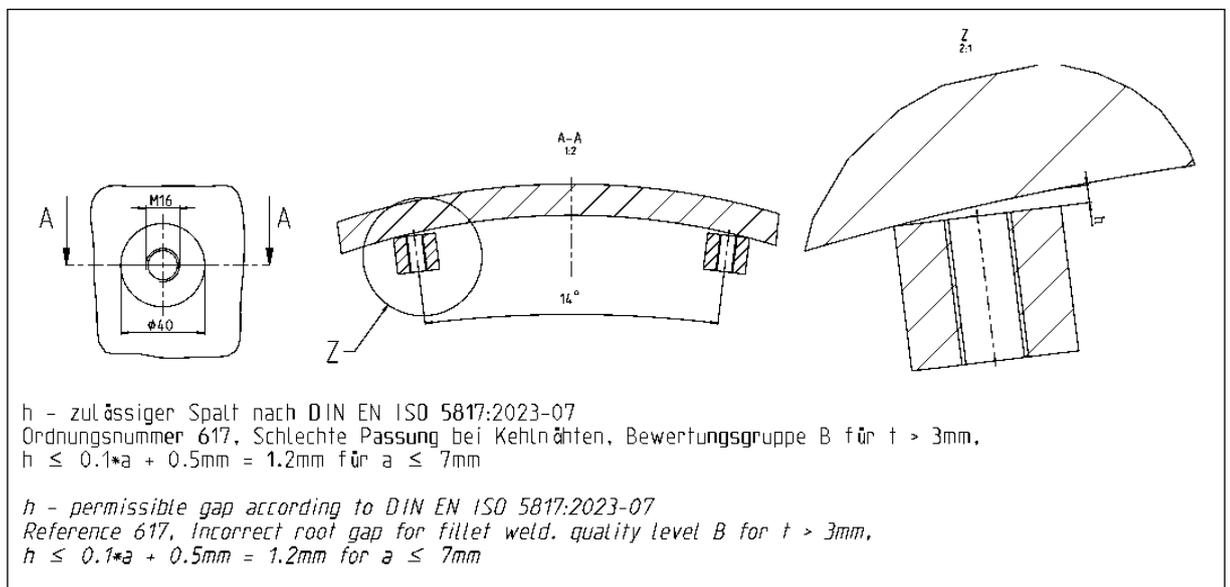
Detail Anschweißbuchse für Leiter auf gekrümmten Mantelblechen
